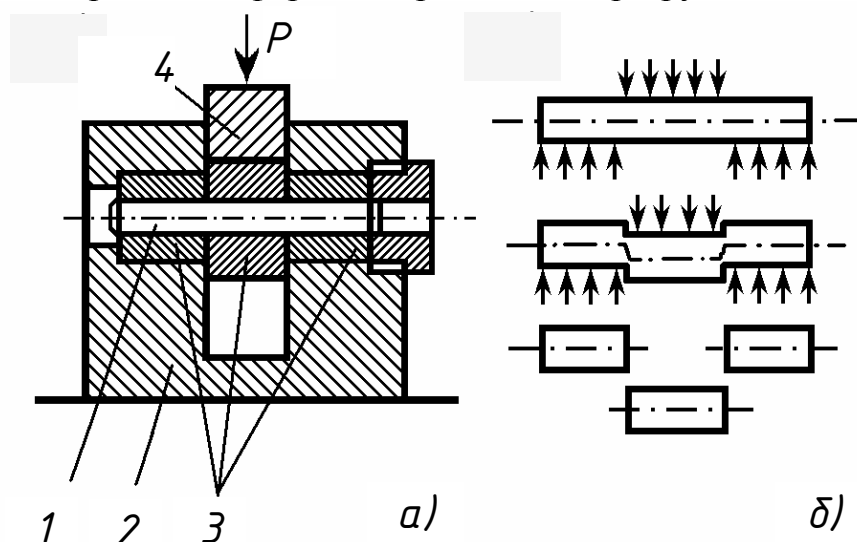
Приспособление для проведения испытаний (а) и схема загрузки образца (б) при срезе
